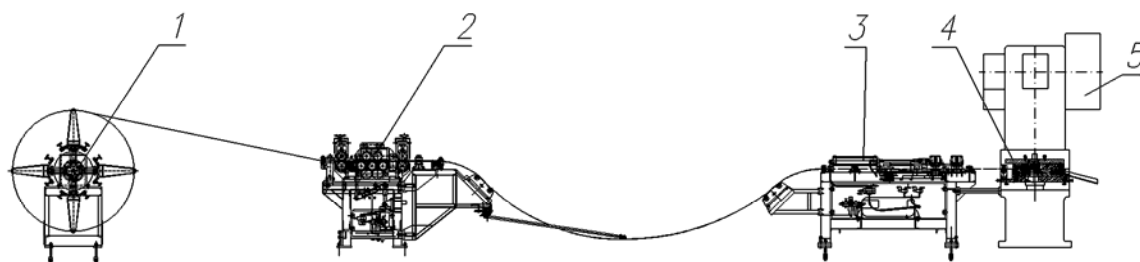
Линия штамповки детали “Консоль”: 1 – разматыватель рулона, 2 – машина листопрямляющая, 3 – устройство шаговой подачи, 4 – штамп комбинированный, 5 – пресс кривошипный
